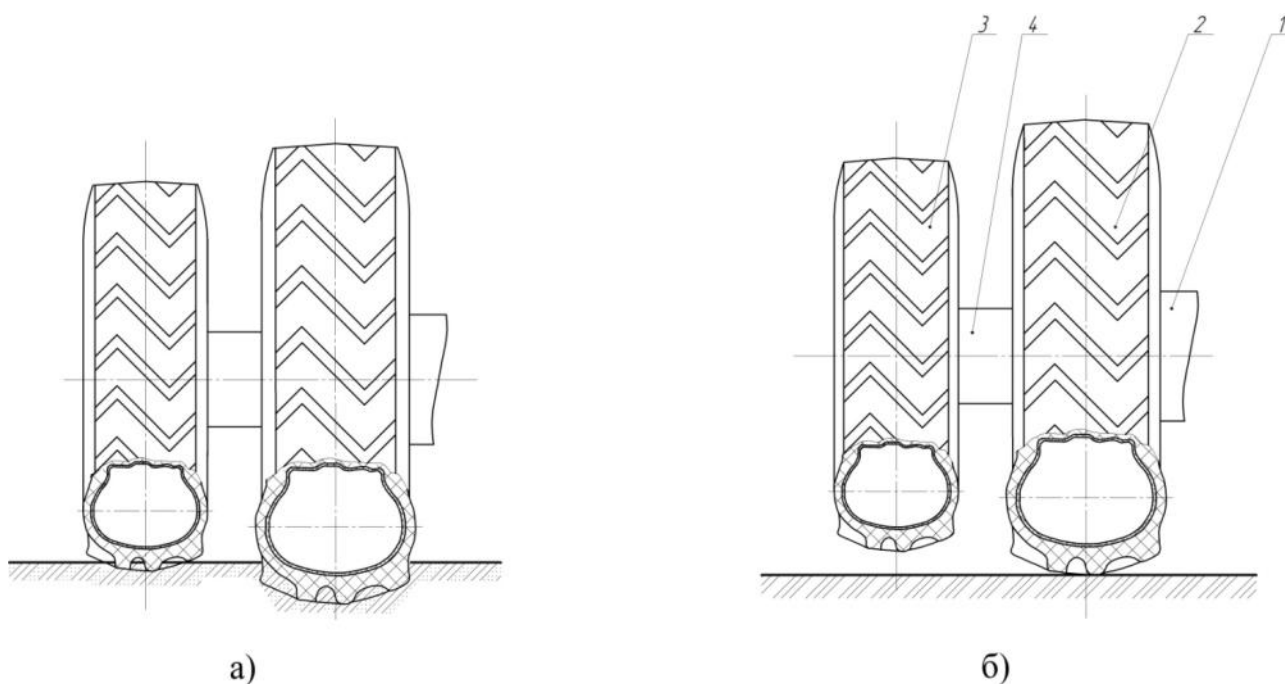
Сдвоенные ведущие колёса разного диаметра при движении по деформирующейся а, и твёрдой опорной поверхности б: 1 – ступица колеса; 2 – основное колесо с пневматической шиной; 3 – дополнительное колесо с пневматической шиной меньшего диаметра; 4 – соединительный диск.
